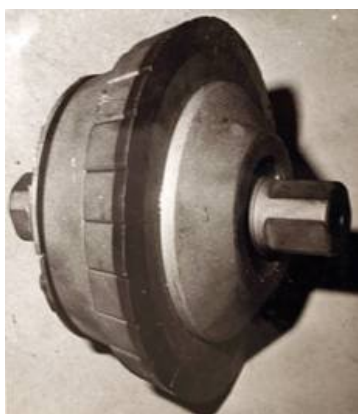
Общий вид СВР для проходческих комбайнов с твердосплавной опорой вращения и набором быстросменных твердосплавных ножей
